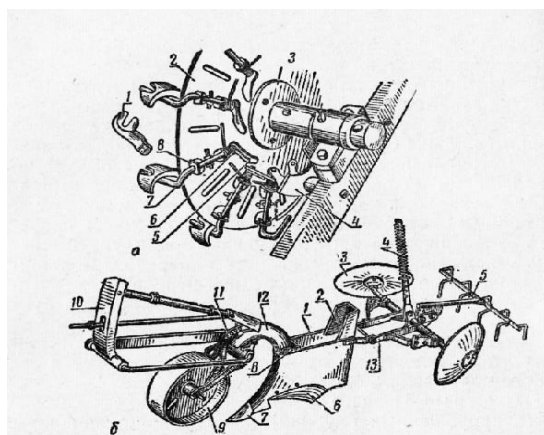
Основные узлы картофелепосадочной машины: а — вычерпывающий аппарат ложечно-дискового типа: 1 — ложечка; 2 — диск; 3 — ступица; 4 — шина; 5 — отводящий рычажок; в — пружина; 7 — зажим; 8 — кронштейн; б — сошниковая группа: 1 — корпус сошника; 2 — приемный ковш; 3 — заделывающий диск; 4 — нажимная
